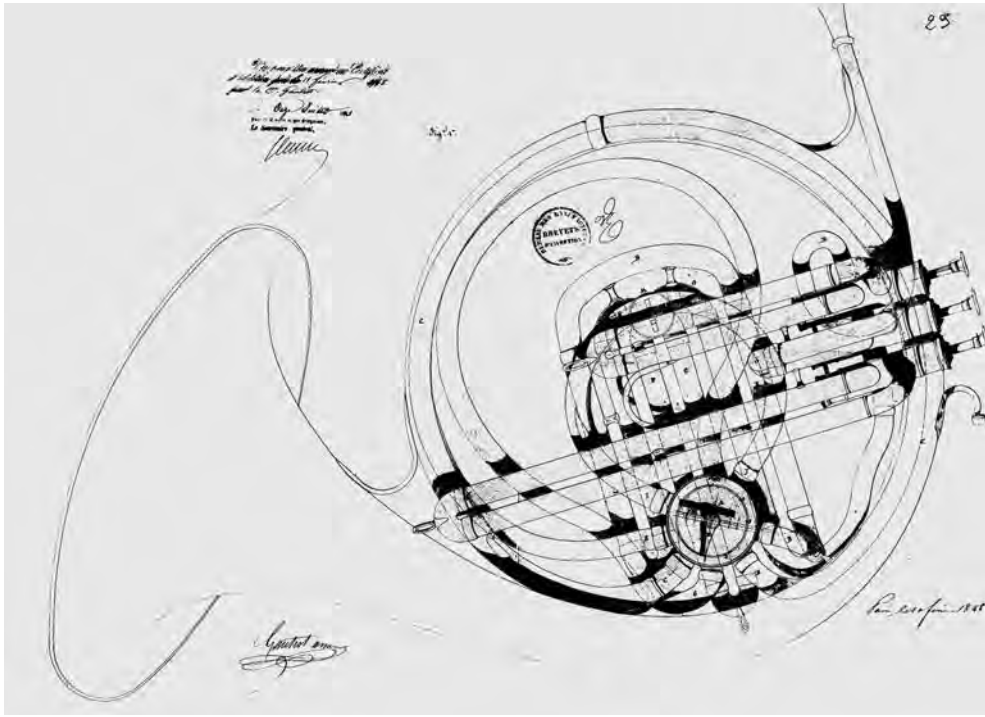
Dessin de la deuxième addition du 11 février 1848 au brevet 5874, planche 1
